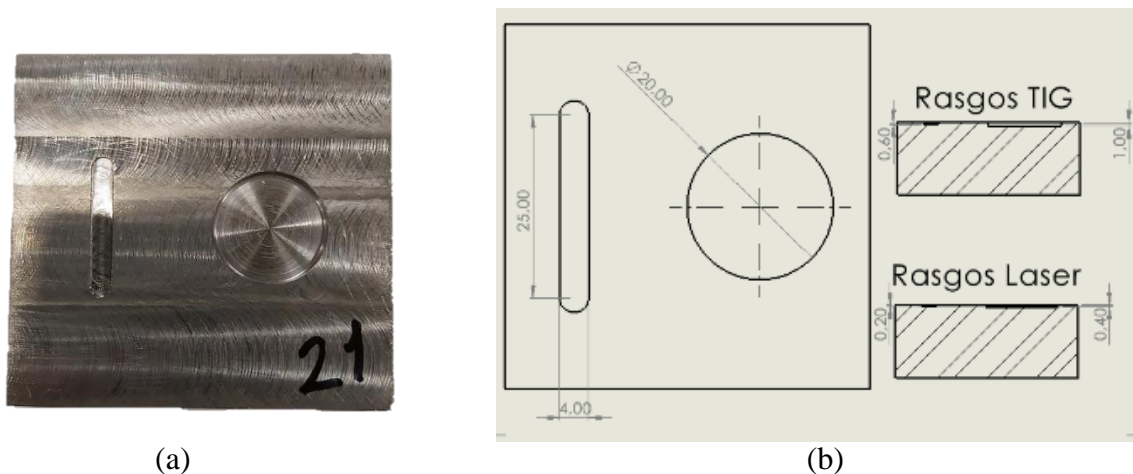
Geometria dos provetes para soldadura TIG e Laser Nd:YAG: (a) Provede após maquinação dos rasgos; (b) Desenho CAD dos rasgos
